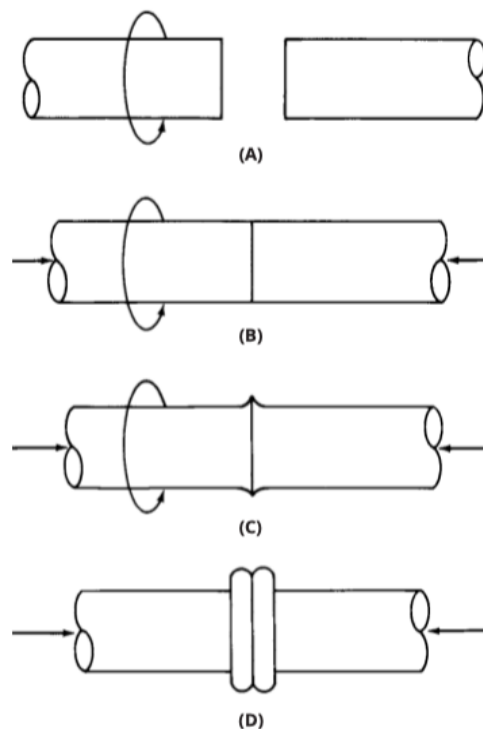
Secuencia básica de soldadura por fricción
